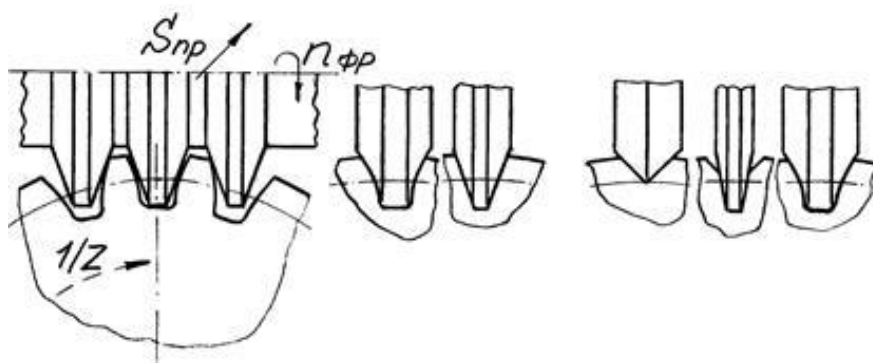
Схема обработки зубьев набором дисковых угловых фрез и их профили
